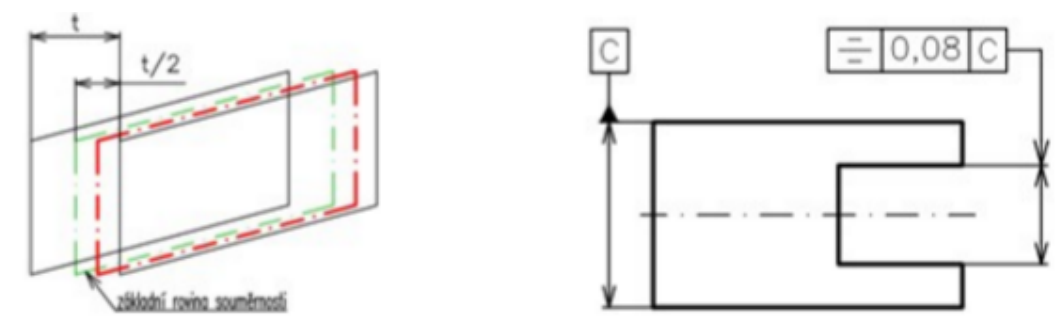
Zobrazení tolerance umístění na výkresové dokumentaci [3]
